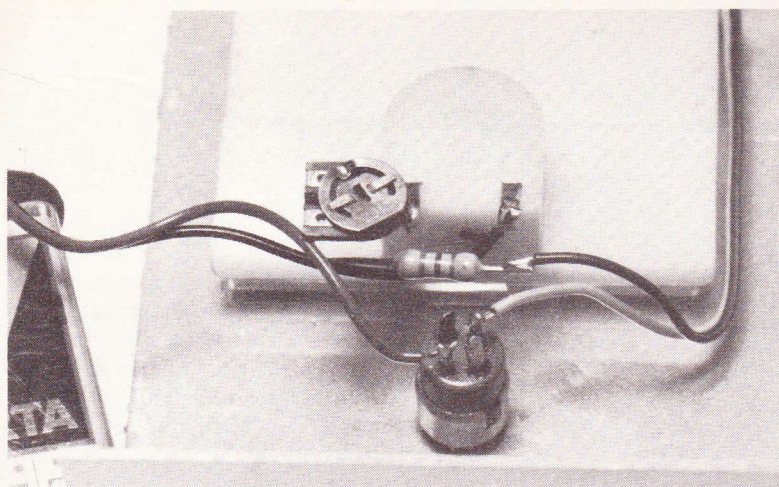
Gros plan sur les éléments câblés en l'air, du testeur d'humidité.
